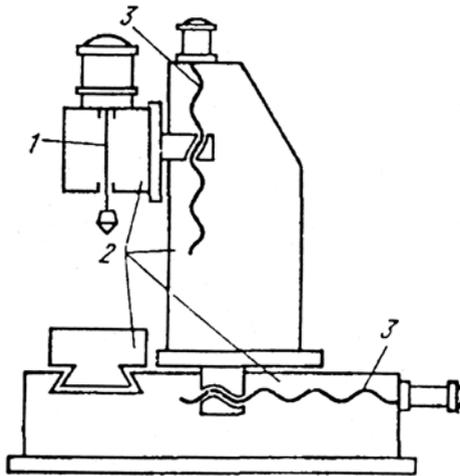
Основные узлы (сборочные единицы) станка: 1 – главный привод; 2 – базовые детали; 3 – приводы подачи.
